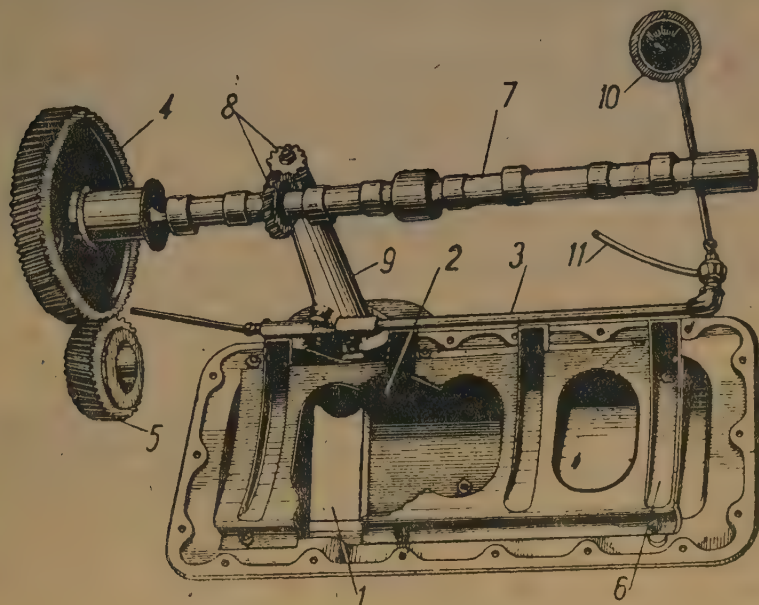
Схема смазки подшипников коленчатого вала разбрызгиванием:
